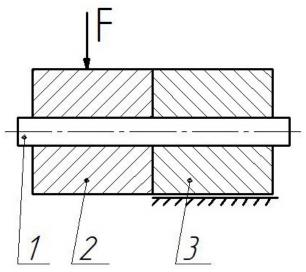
Конструктивная схема отрезки сдвигом [1]
